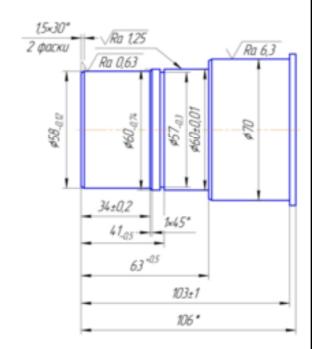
Общий вид переходника до механической обработки перед сваркой и после сварки в составе оси
